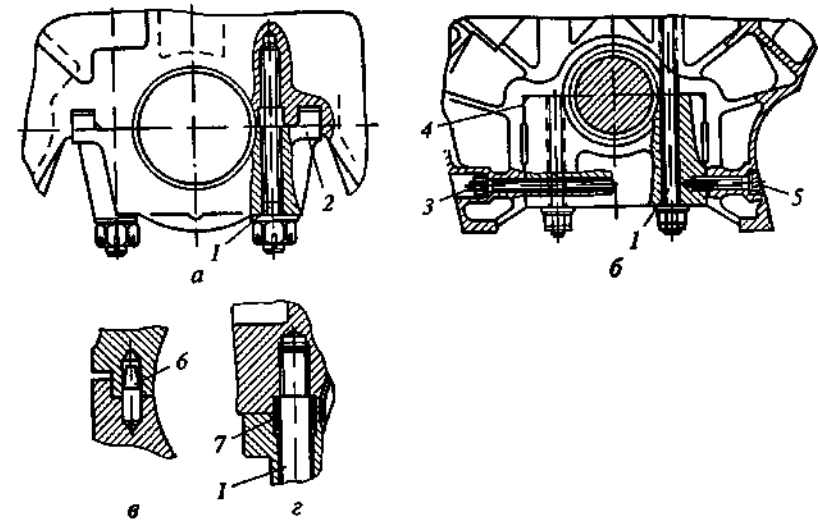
Крепление крышек коренных подшипников коленчатого вала с использованием фиксирующих элементов: а — выступов; б — поверхностей и стяжных шпилек; в — штифтов; г — втулок; 1 — основная силовая шпилька; 2 — фиксирующие выступы крышки; 3 — стяжная сквозная шпилька; 4 — фиксирующая поверхность; 5 — ртяжной болт; 6 — штифт; 7 — втулка
